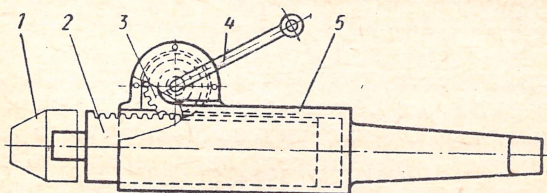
Приспособление к токарному станку для безопасного сверления отверстий
